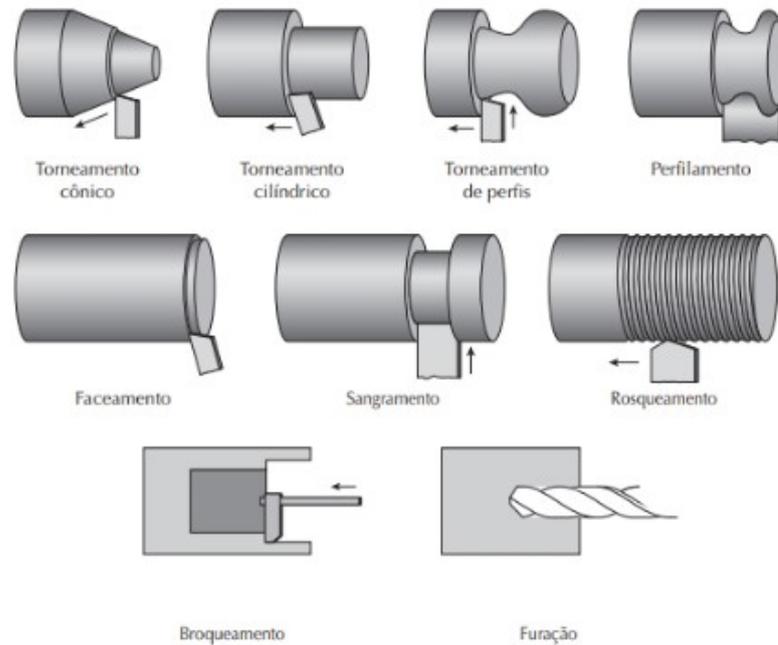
Principais operações de usinagem que podem ser realizadas nos tornos.
